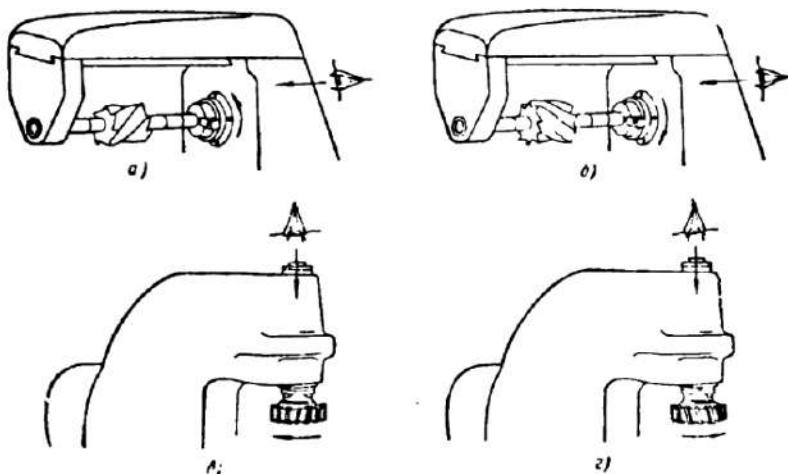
Концевые фрезы с винтовыми канавками, транспортирующими стружку:
